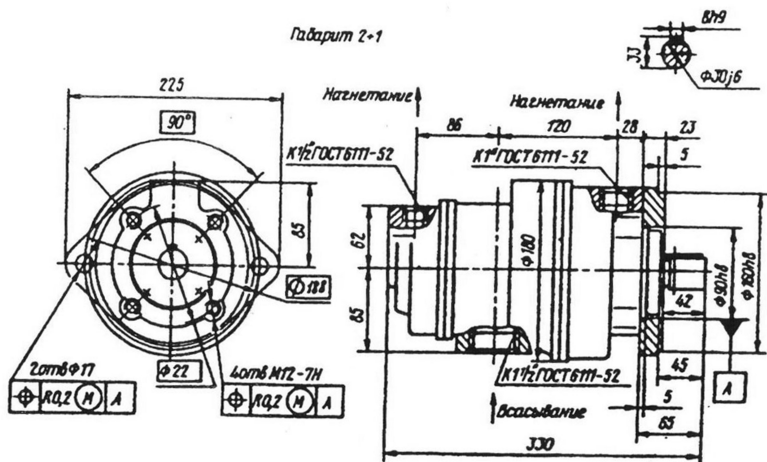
Габаритные и присоединительные размеры насосов 5Г12-24АМ...35Г12-25АМ
